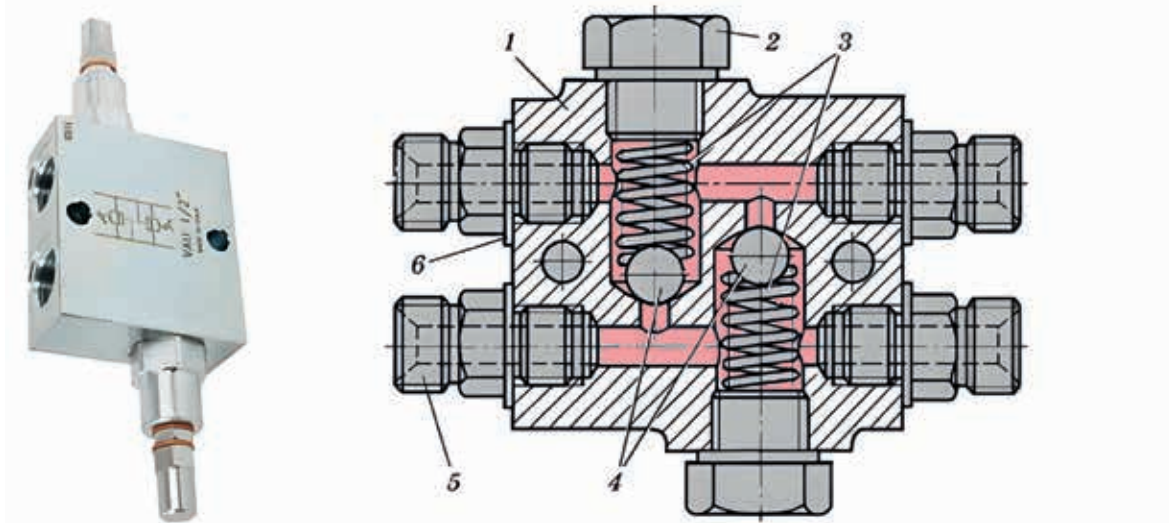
Загальний вигляд і схема подвійного запобіжного клапана: 1 – корпус; 2 – пробка; 3 – пружина; 4 – кулька; 5 – штуцер; 6 – прокладка
